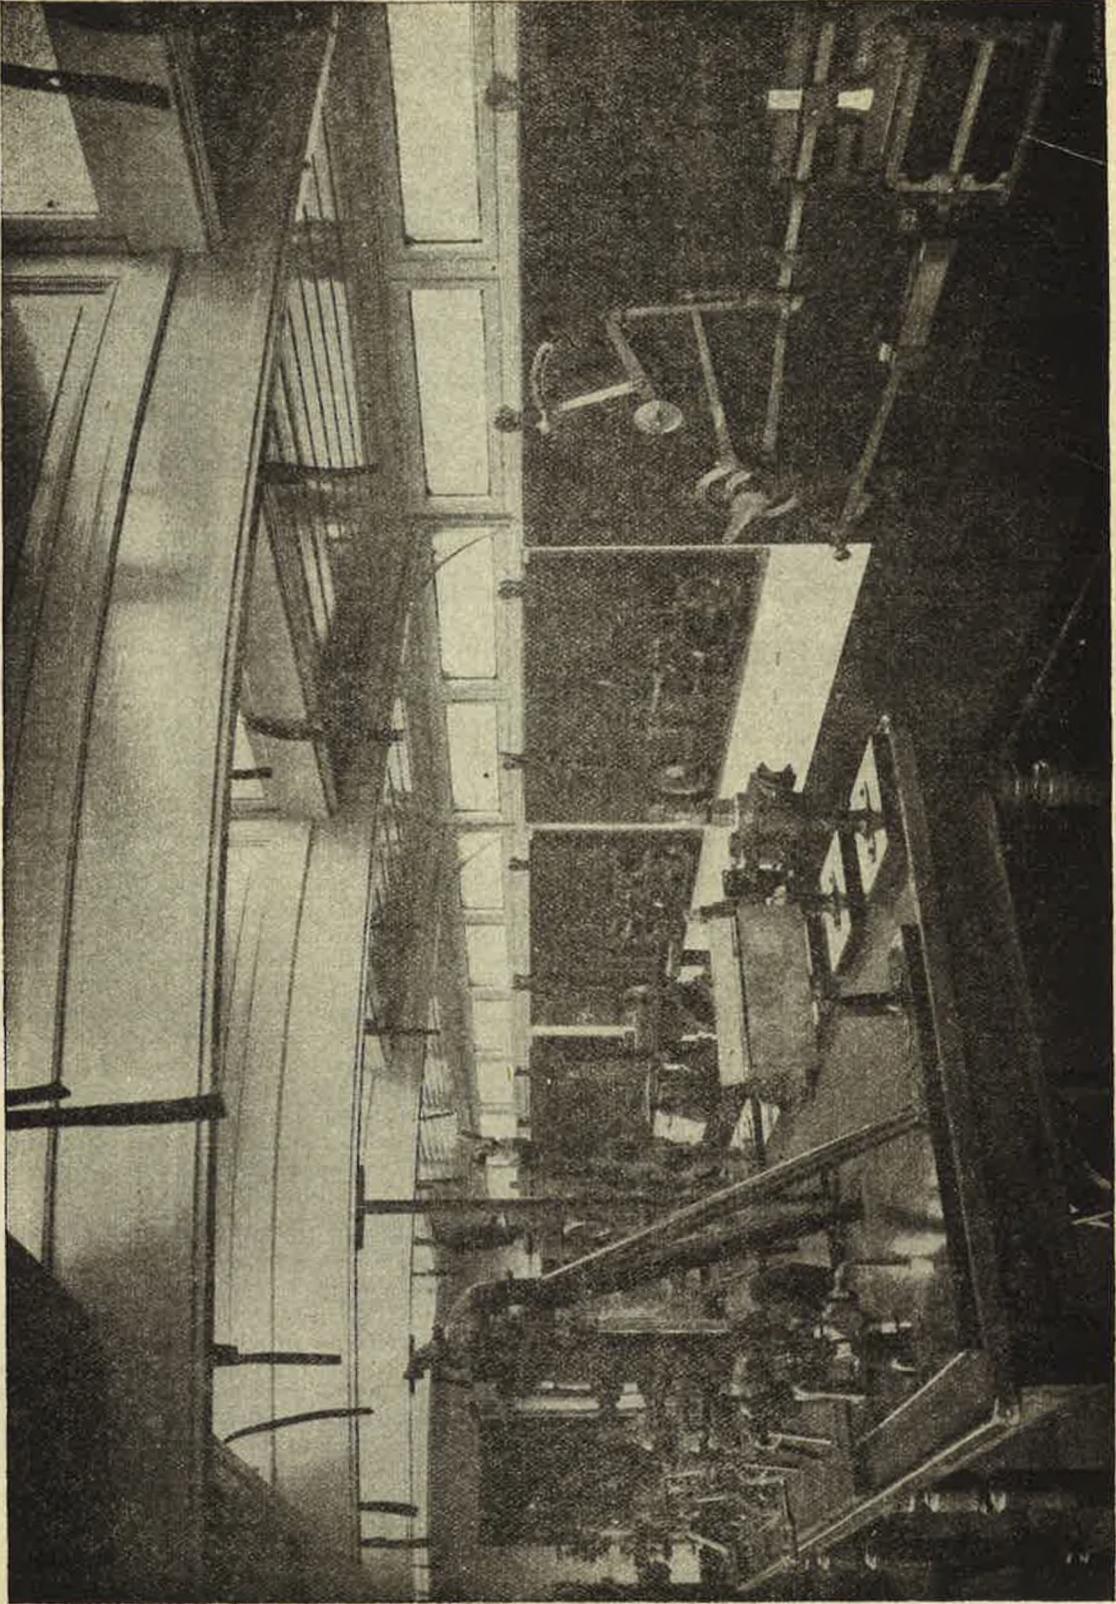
Vue d'ensemble de la salle de démonstration de la première voiture.
